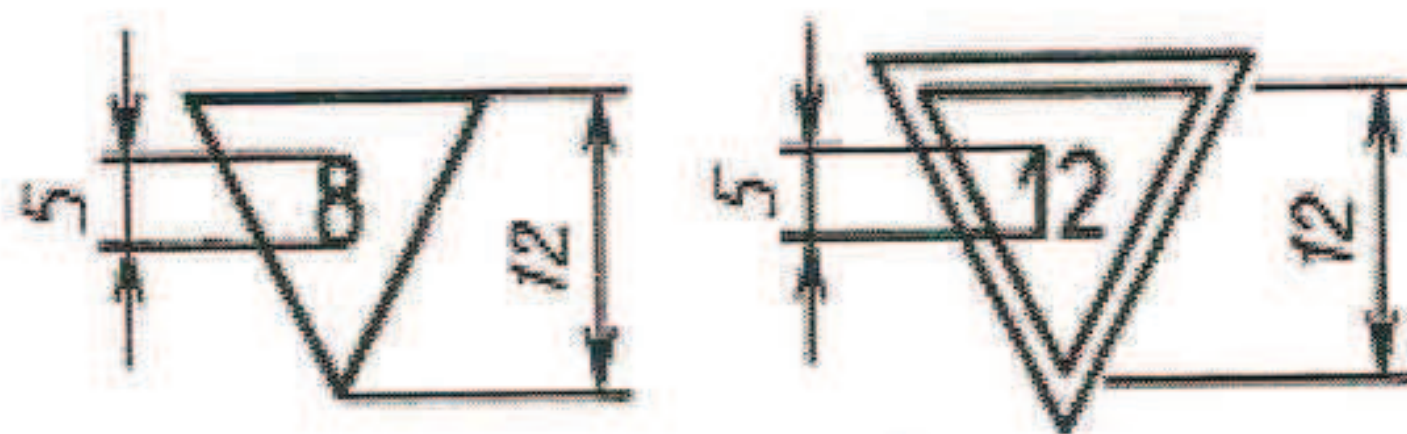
а – Размеры штампа при маркировке закаленного стекла
